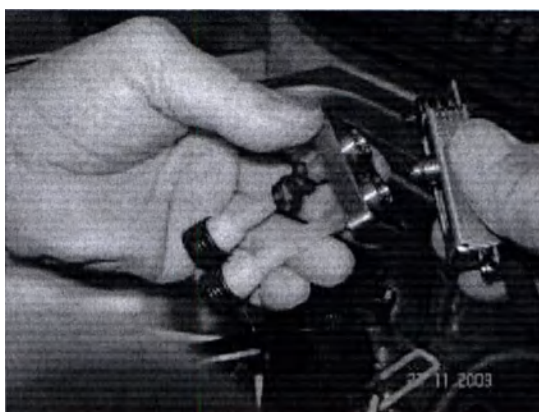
Установка соединителя адаптера на коннектор репроцессора
